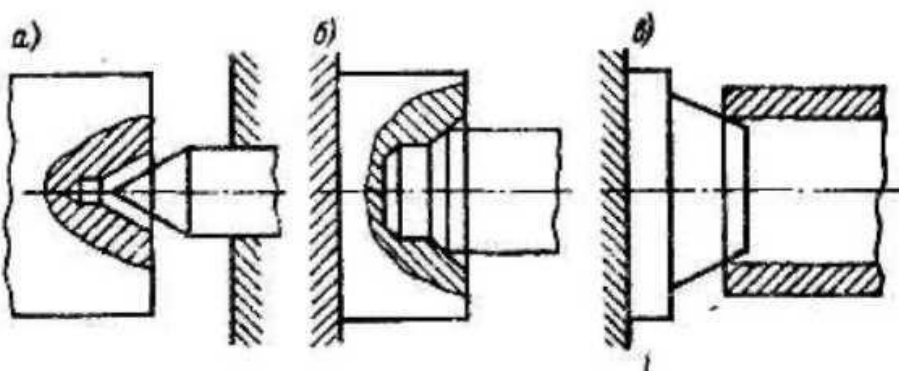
Установка на конусы деталей типа «вал» (а и б), втулок и труб (в)
